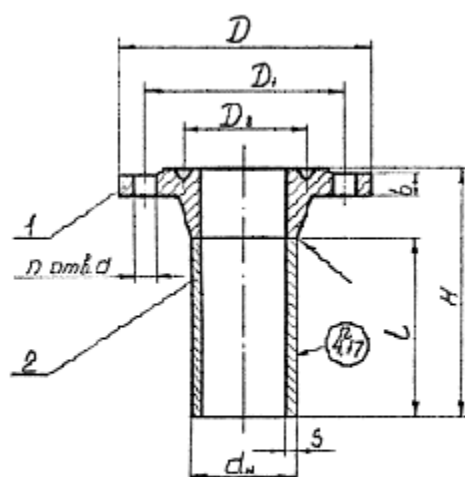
Штуцер с фланцами стальными приварными встык с уплотнительной поверхностью под прокладку овального сечения на условное давление от 6,3 до 16,0 МПа
